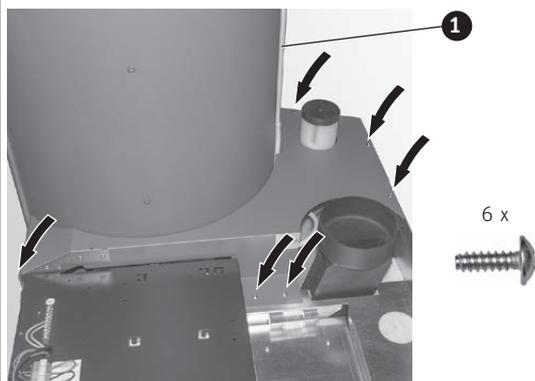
Fissare il rivestimento con 6 viti autofilettanti
